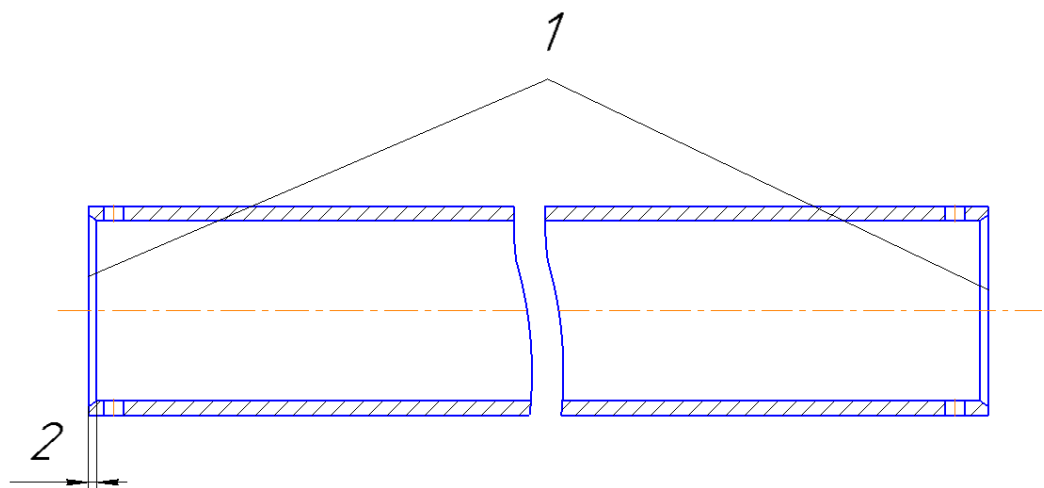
Креслення оброблюваної деталі з необхідними розмірами
